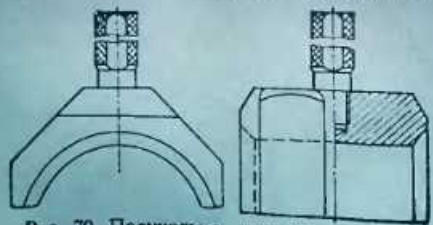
Полукольцо для проверки цилиндричности и перпендикулярности торцов шеек вала
